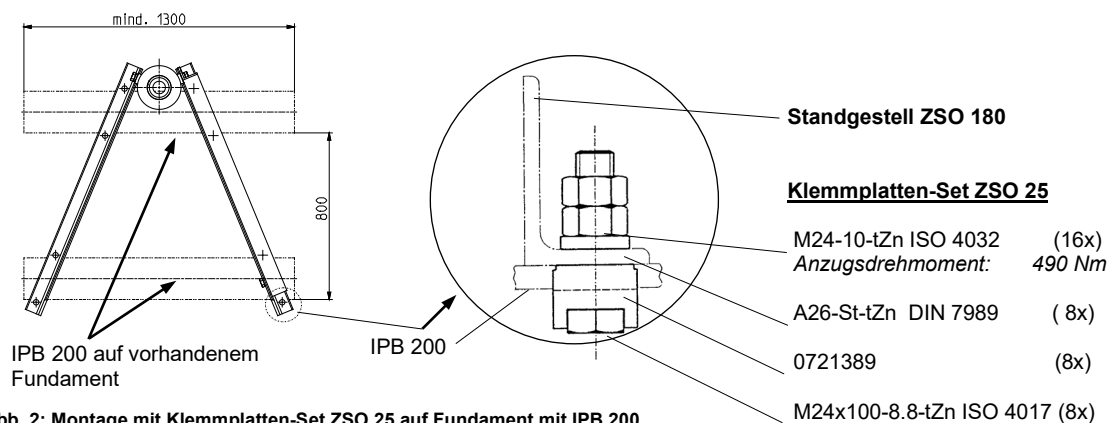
Montage mit Klemmplatten-Set ZSO 25 auf Fundament mit IPB 200
